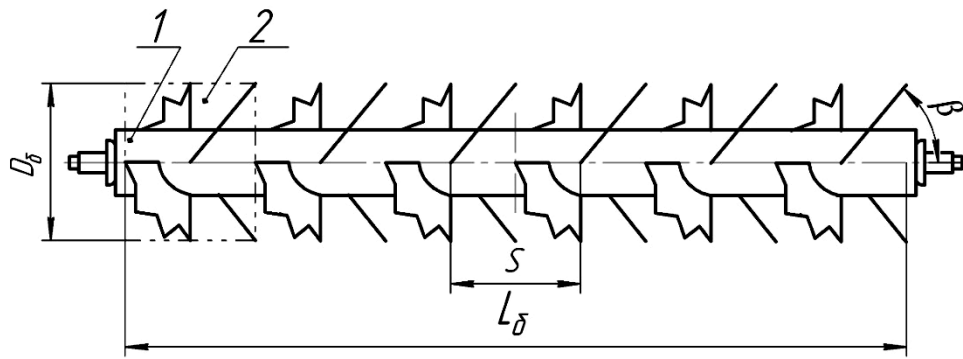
Загальний вид РБ з 6-ма чвертьеліпсними розподілювачами:
